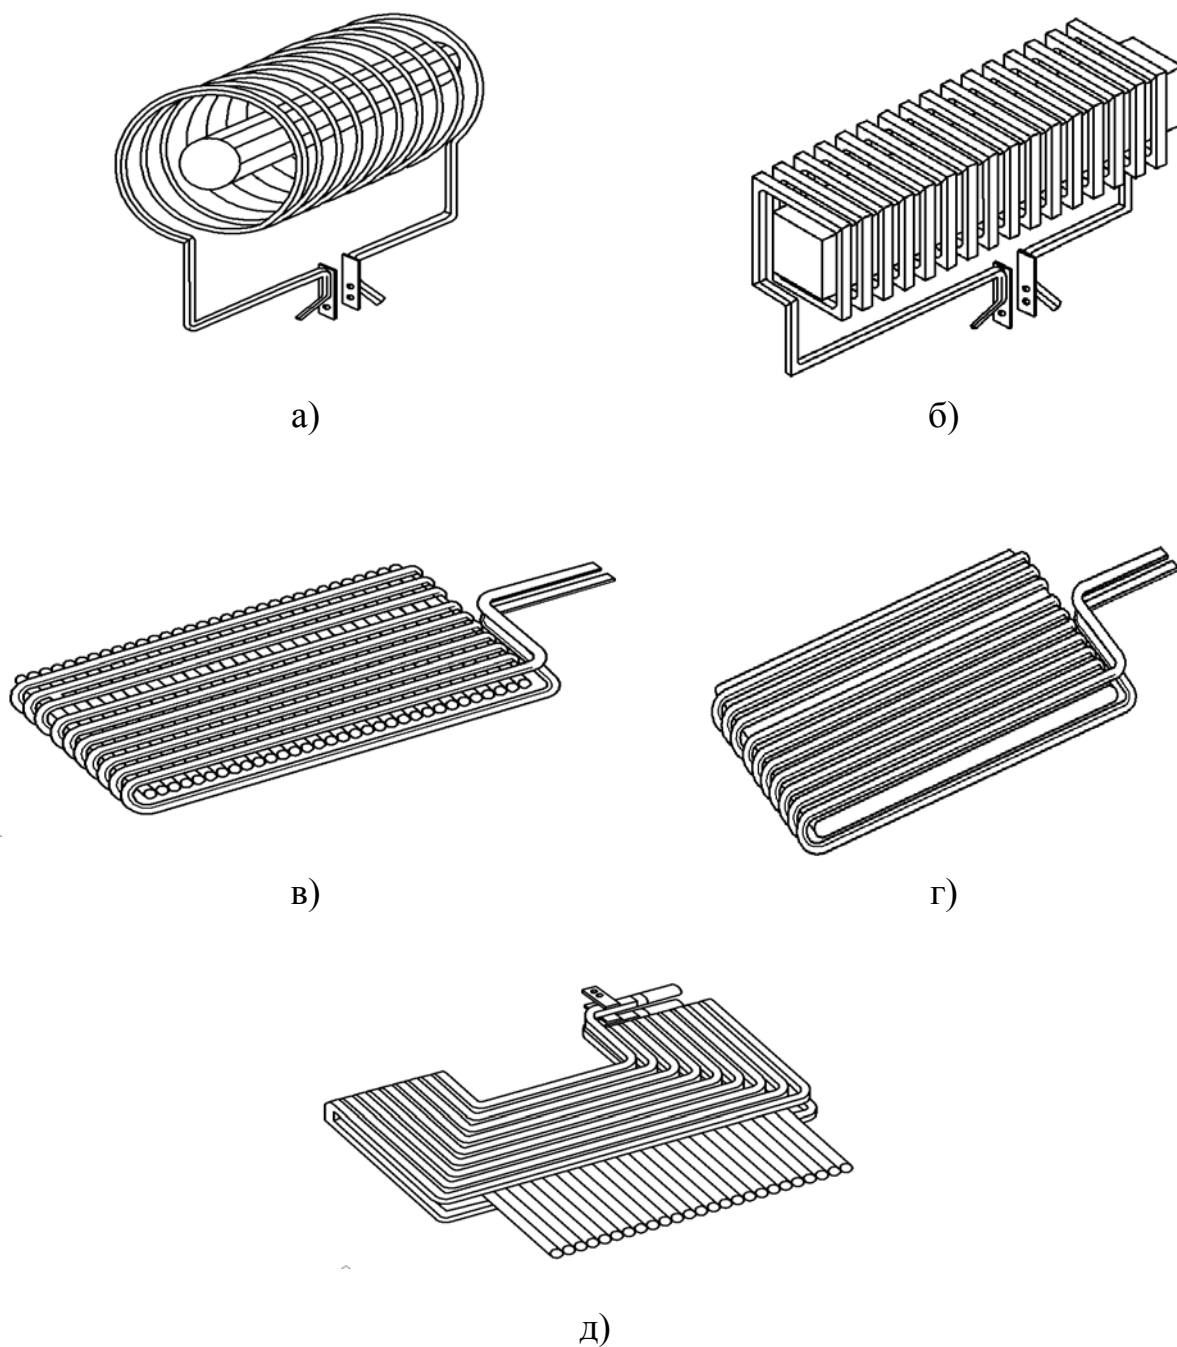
Основные схемы индукторов, применяемых для нагрева кузнечных заготовок: а) цилиндрический; б) квадратный; в) и г) овальный; д) щелевой
